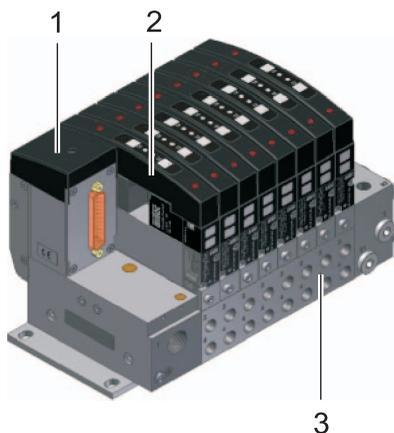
RE-46/08-M-1-000 inkl. RE-46-B-01, BefestigungsfüÙe für Flanschmontage
